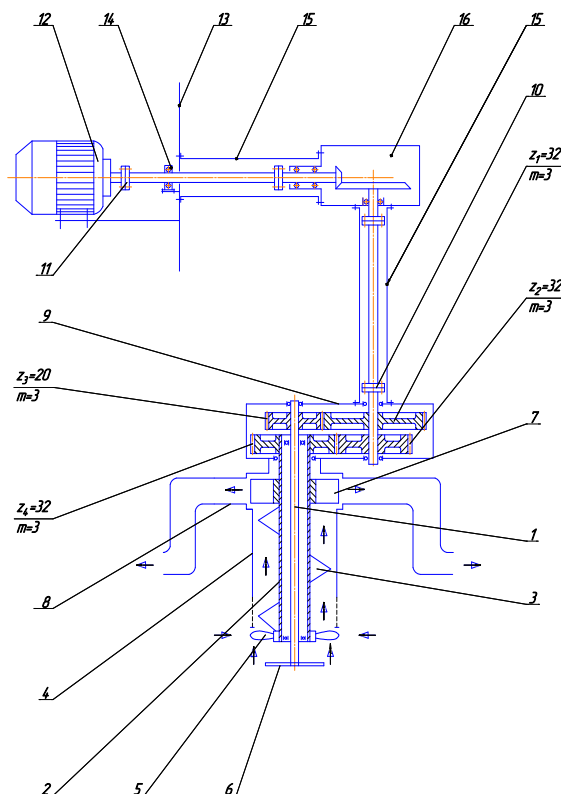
Кінематична схема привода проектного насоса: 1 – внутрішній вал; 2 – вал шнека; 3 – шнекова навивка; 4 – кожух шнека; 5 – перемішувач; 6 – подрібнювач; 7 – лопатевий; 8 – патрубок; 9 – редуктор; 10 – з’єднувальна муфта; 11 – запобіжна муфта; 12 – електродвигун; 13 – стінка реактора; 14 – корпус підшипника; 15 – захисний щиток; 16 – конічний редуктор
